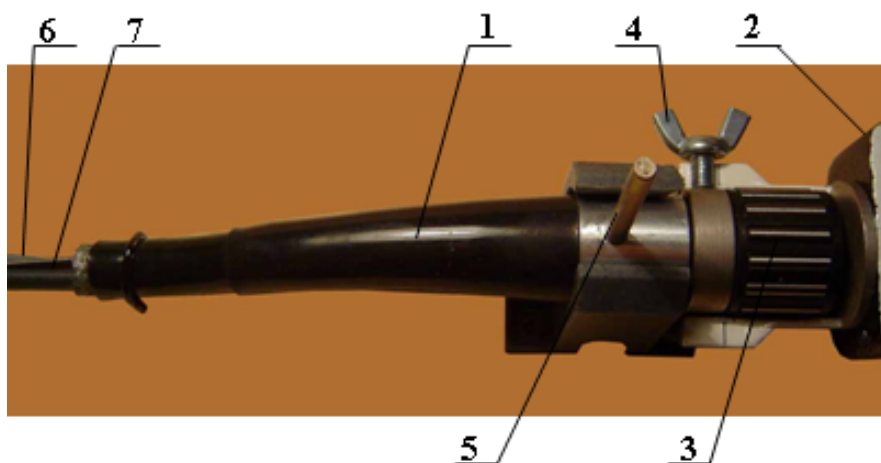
Узел поворота рабочей части вокруг её оси: 1 – рабочая часть; 2 – корпус эндоскопа; 3 – игольчатый подшипник; 4 – винт-фиксатор; 5 – рычаг поворота рабочей части, 6 – жгут изображения, 7 – жгут подсветки
